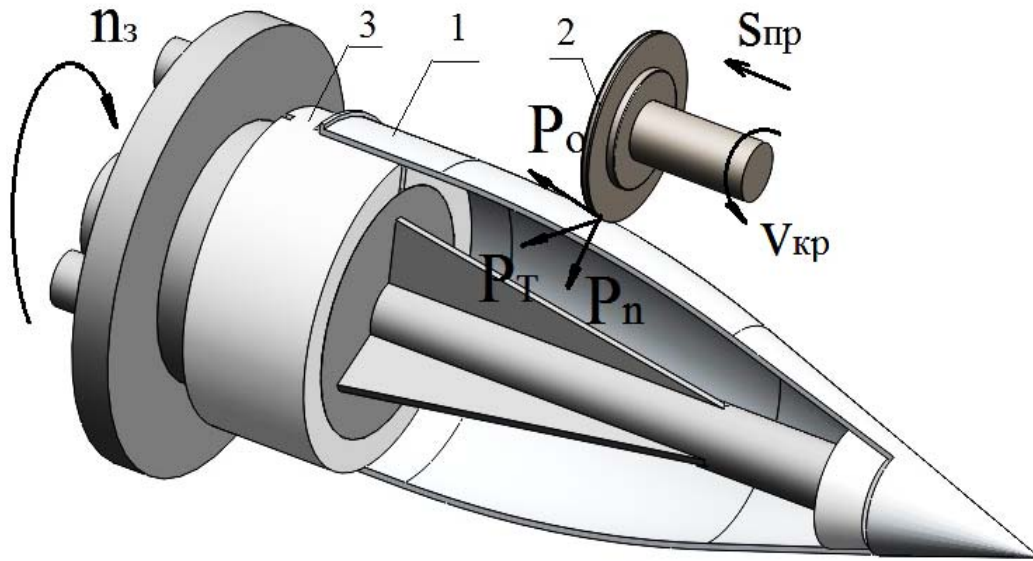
Схема обработки заготовки на операции наружного шлифования изделия
